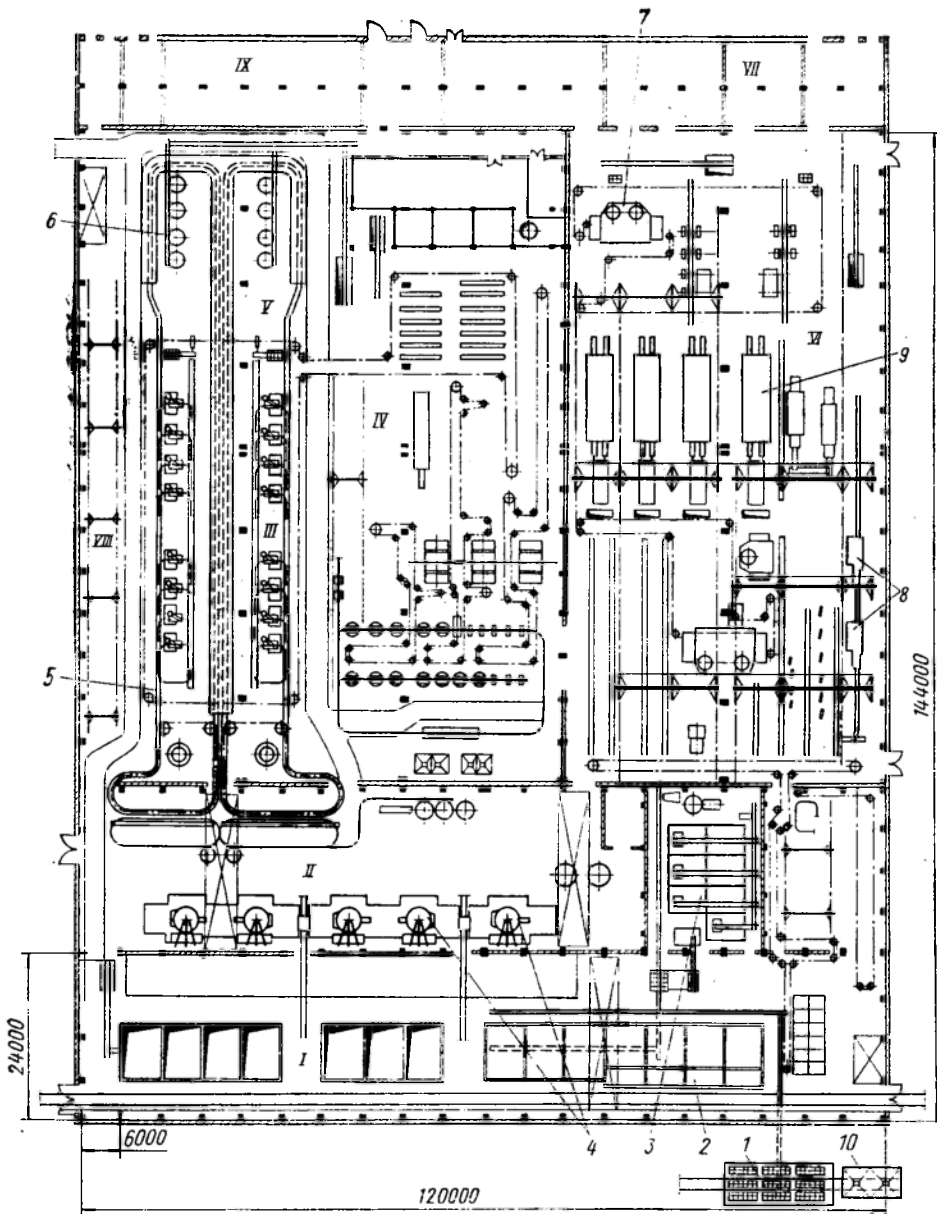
Одноэтажный сталелитейный цех для автомобилестроения:
